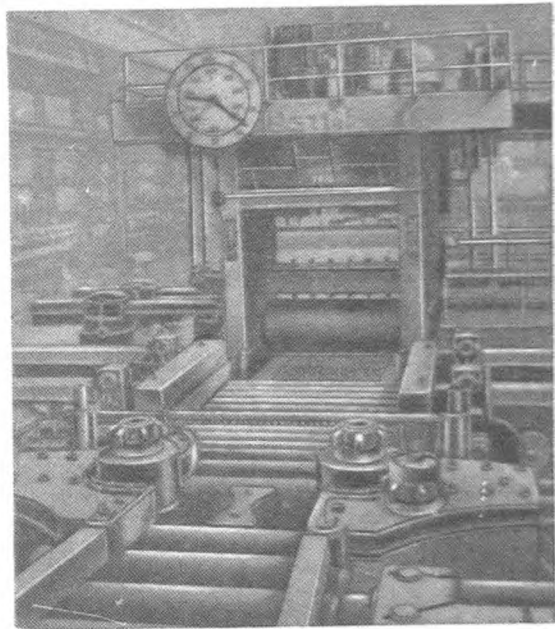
Черновая дуо-реверсивная клеть 1150/2800 (спереди расположены вертикальные валки)
